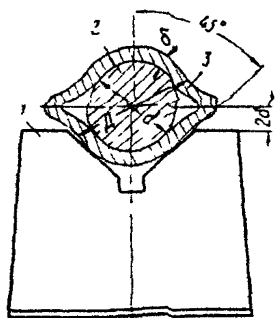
Схема электрода для контактной стыковой сварки арматуры или канатов с напрессованными гильзами
